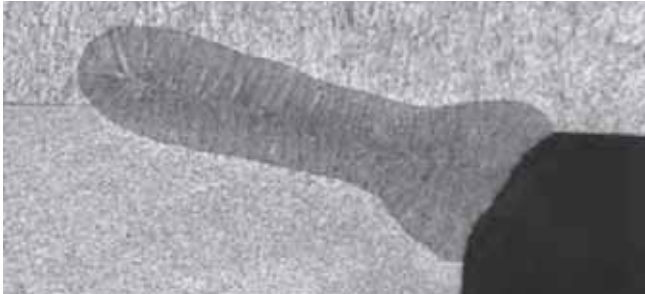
Schliffbild einer Laserschweißnaht
